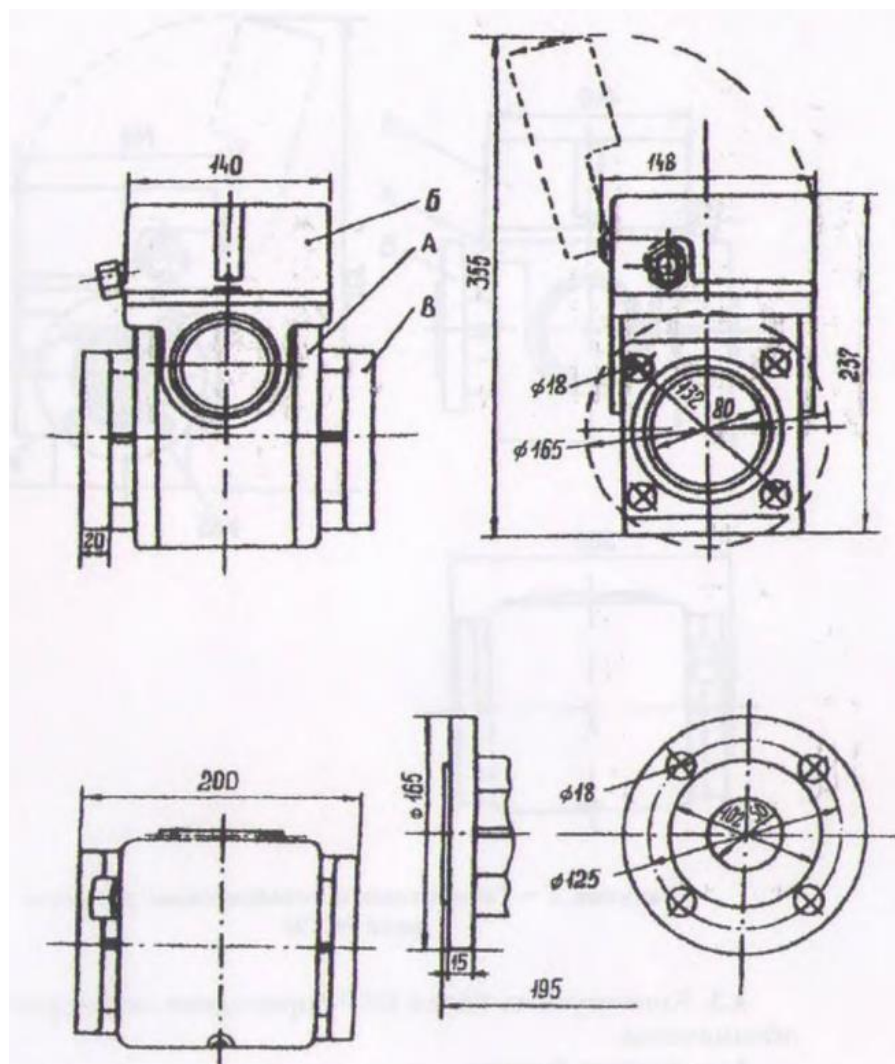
Габаритные и установочные размеры реле РГТ80(50)
